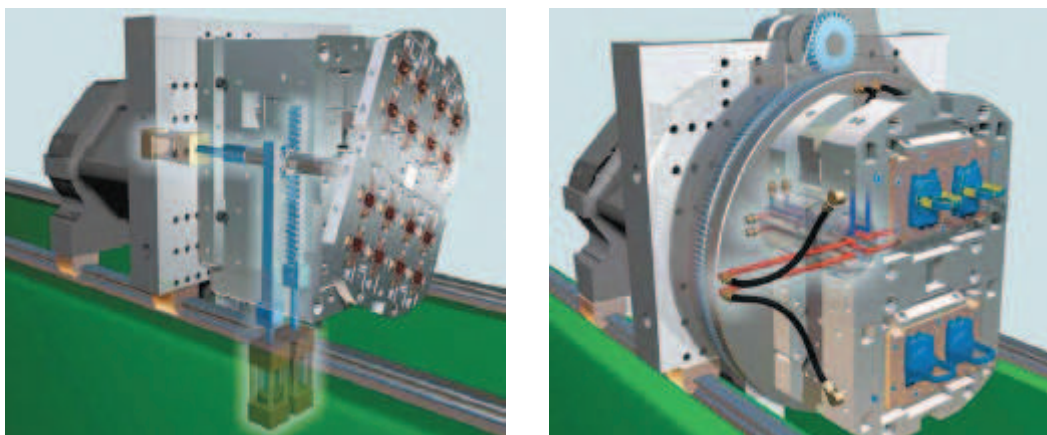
Molde bi-material processo automático – lado esquerdo chapa rotativa, lado direito prato rotativo [15].
